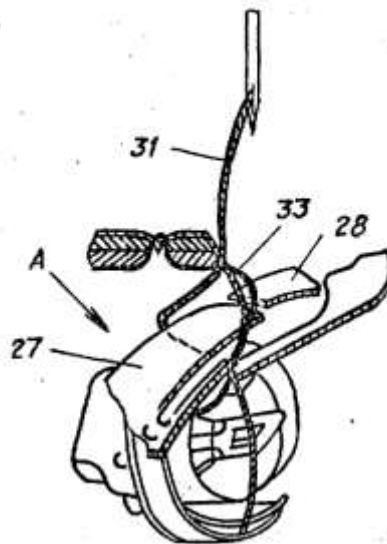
Ножі і розташування ниток, що обрізаються
